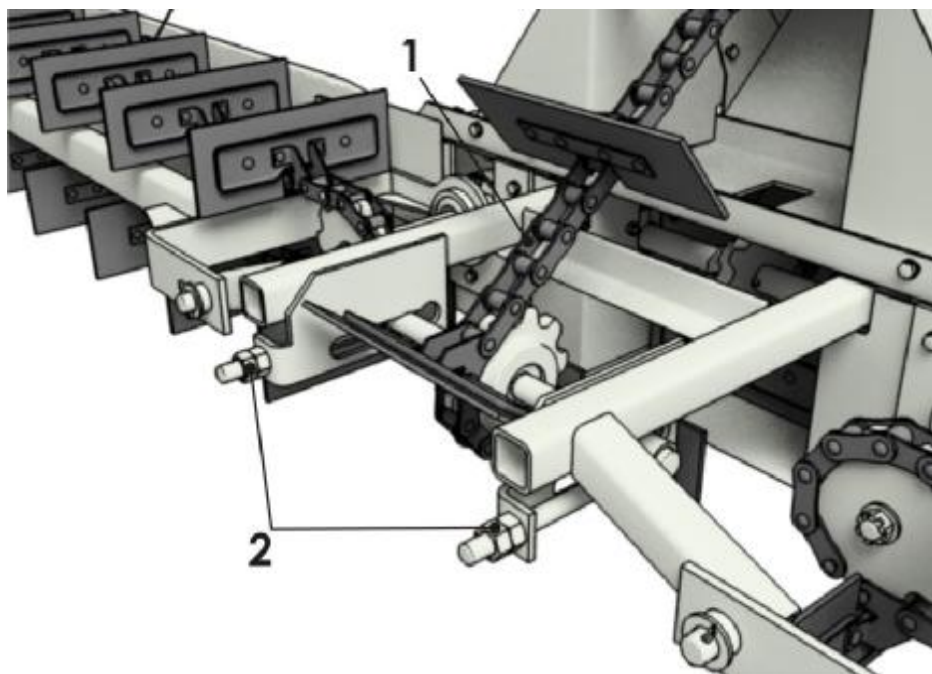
Регулировка натяжения скребковой цепи загрузочного транспортера
